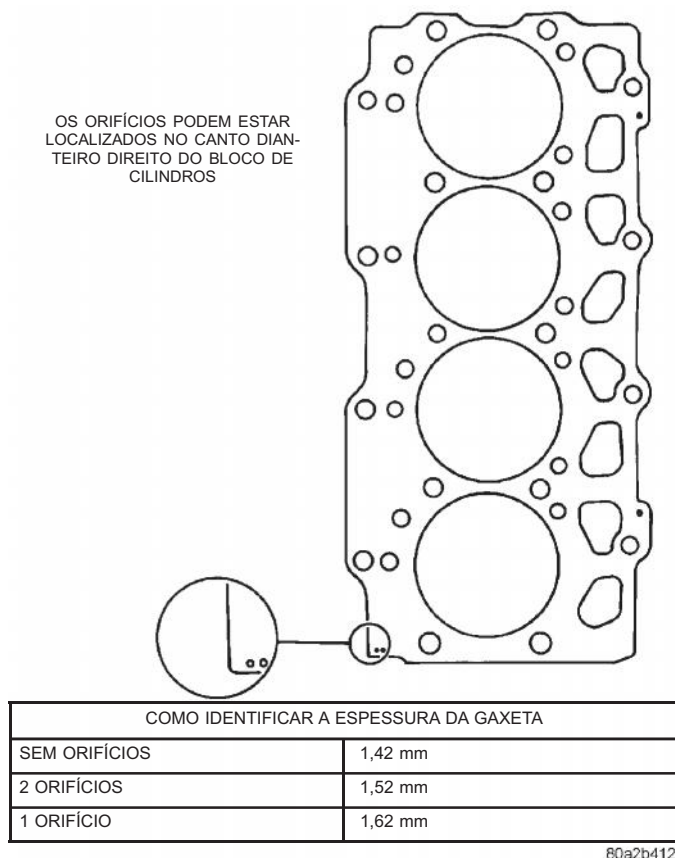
Identificação da Gaxeta de Aço do Cabeçote do Cilindro
